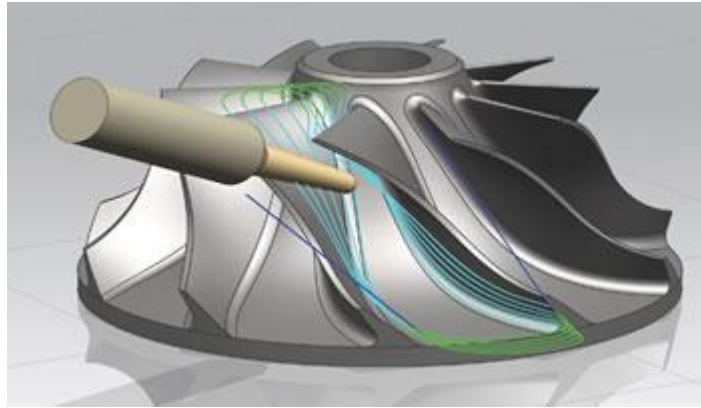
İmpeller kanat üzerinde takım izleri.
